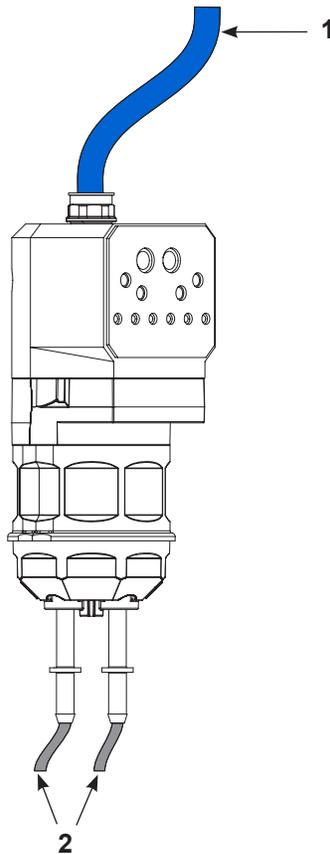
Номера деталей пневмошлангов и порошковых шлангов
